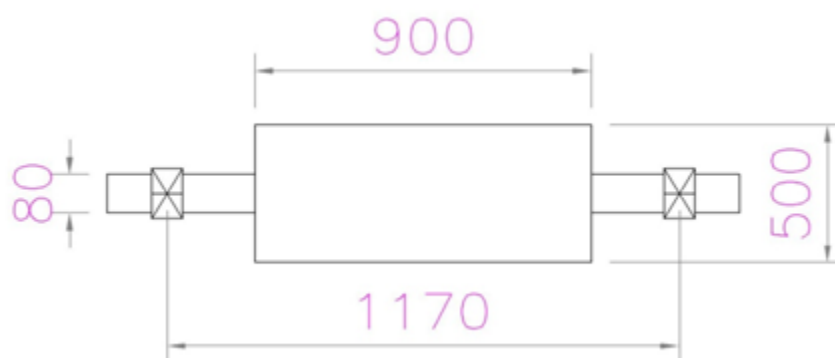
Dimensiones del tambor motriz para la banda BT-1
